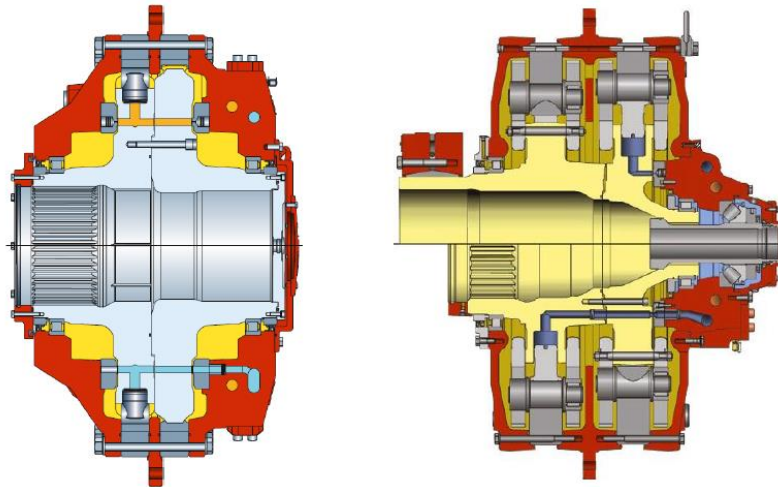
El motor CBM 2000 (lado izquierdo) y el motor MB1600 (lado derecho)
